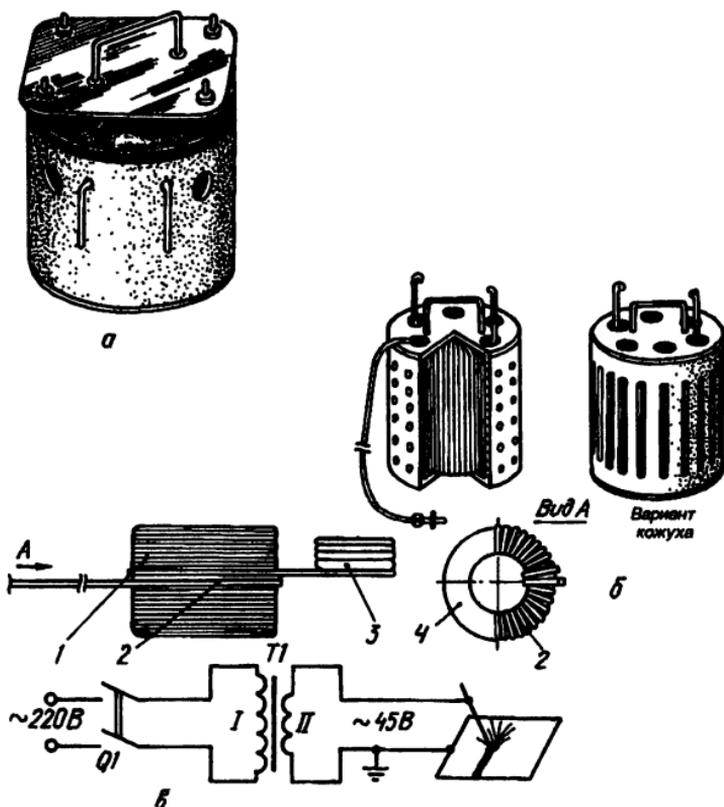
Малогабаритный сварочный аппарат переменного тока:
